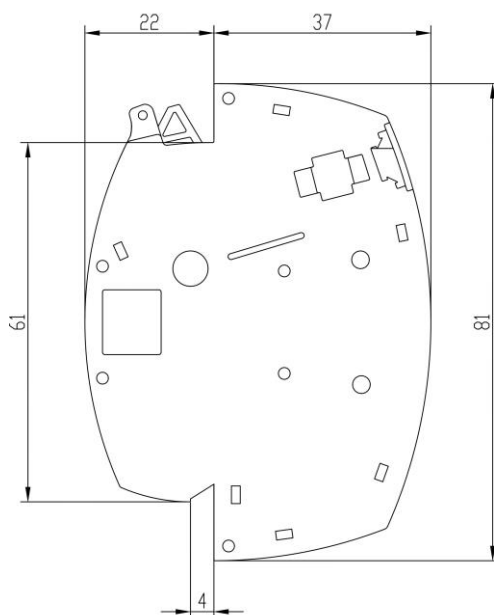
Общий вид базового блока ЭПББ. Вид сбоку.
